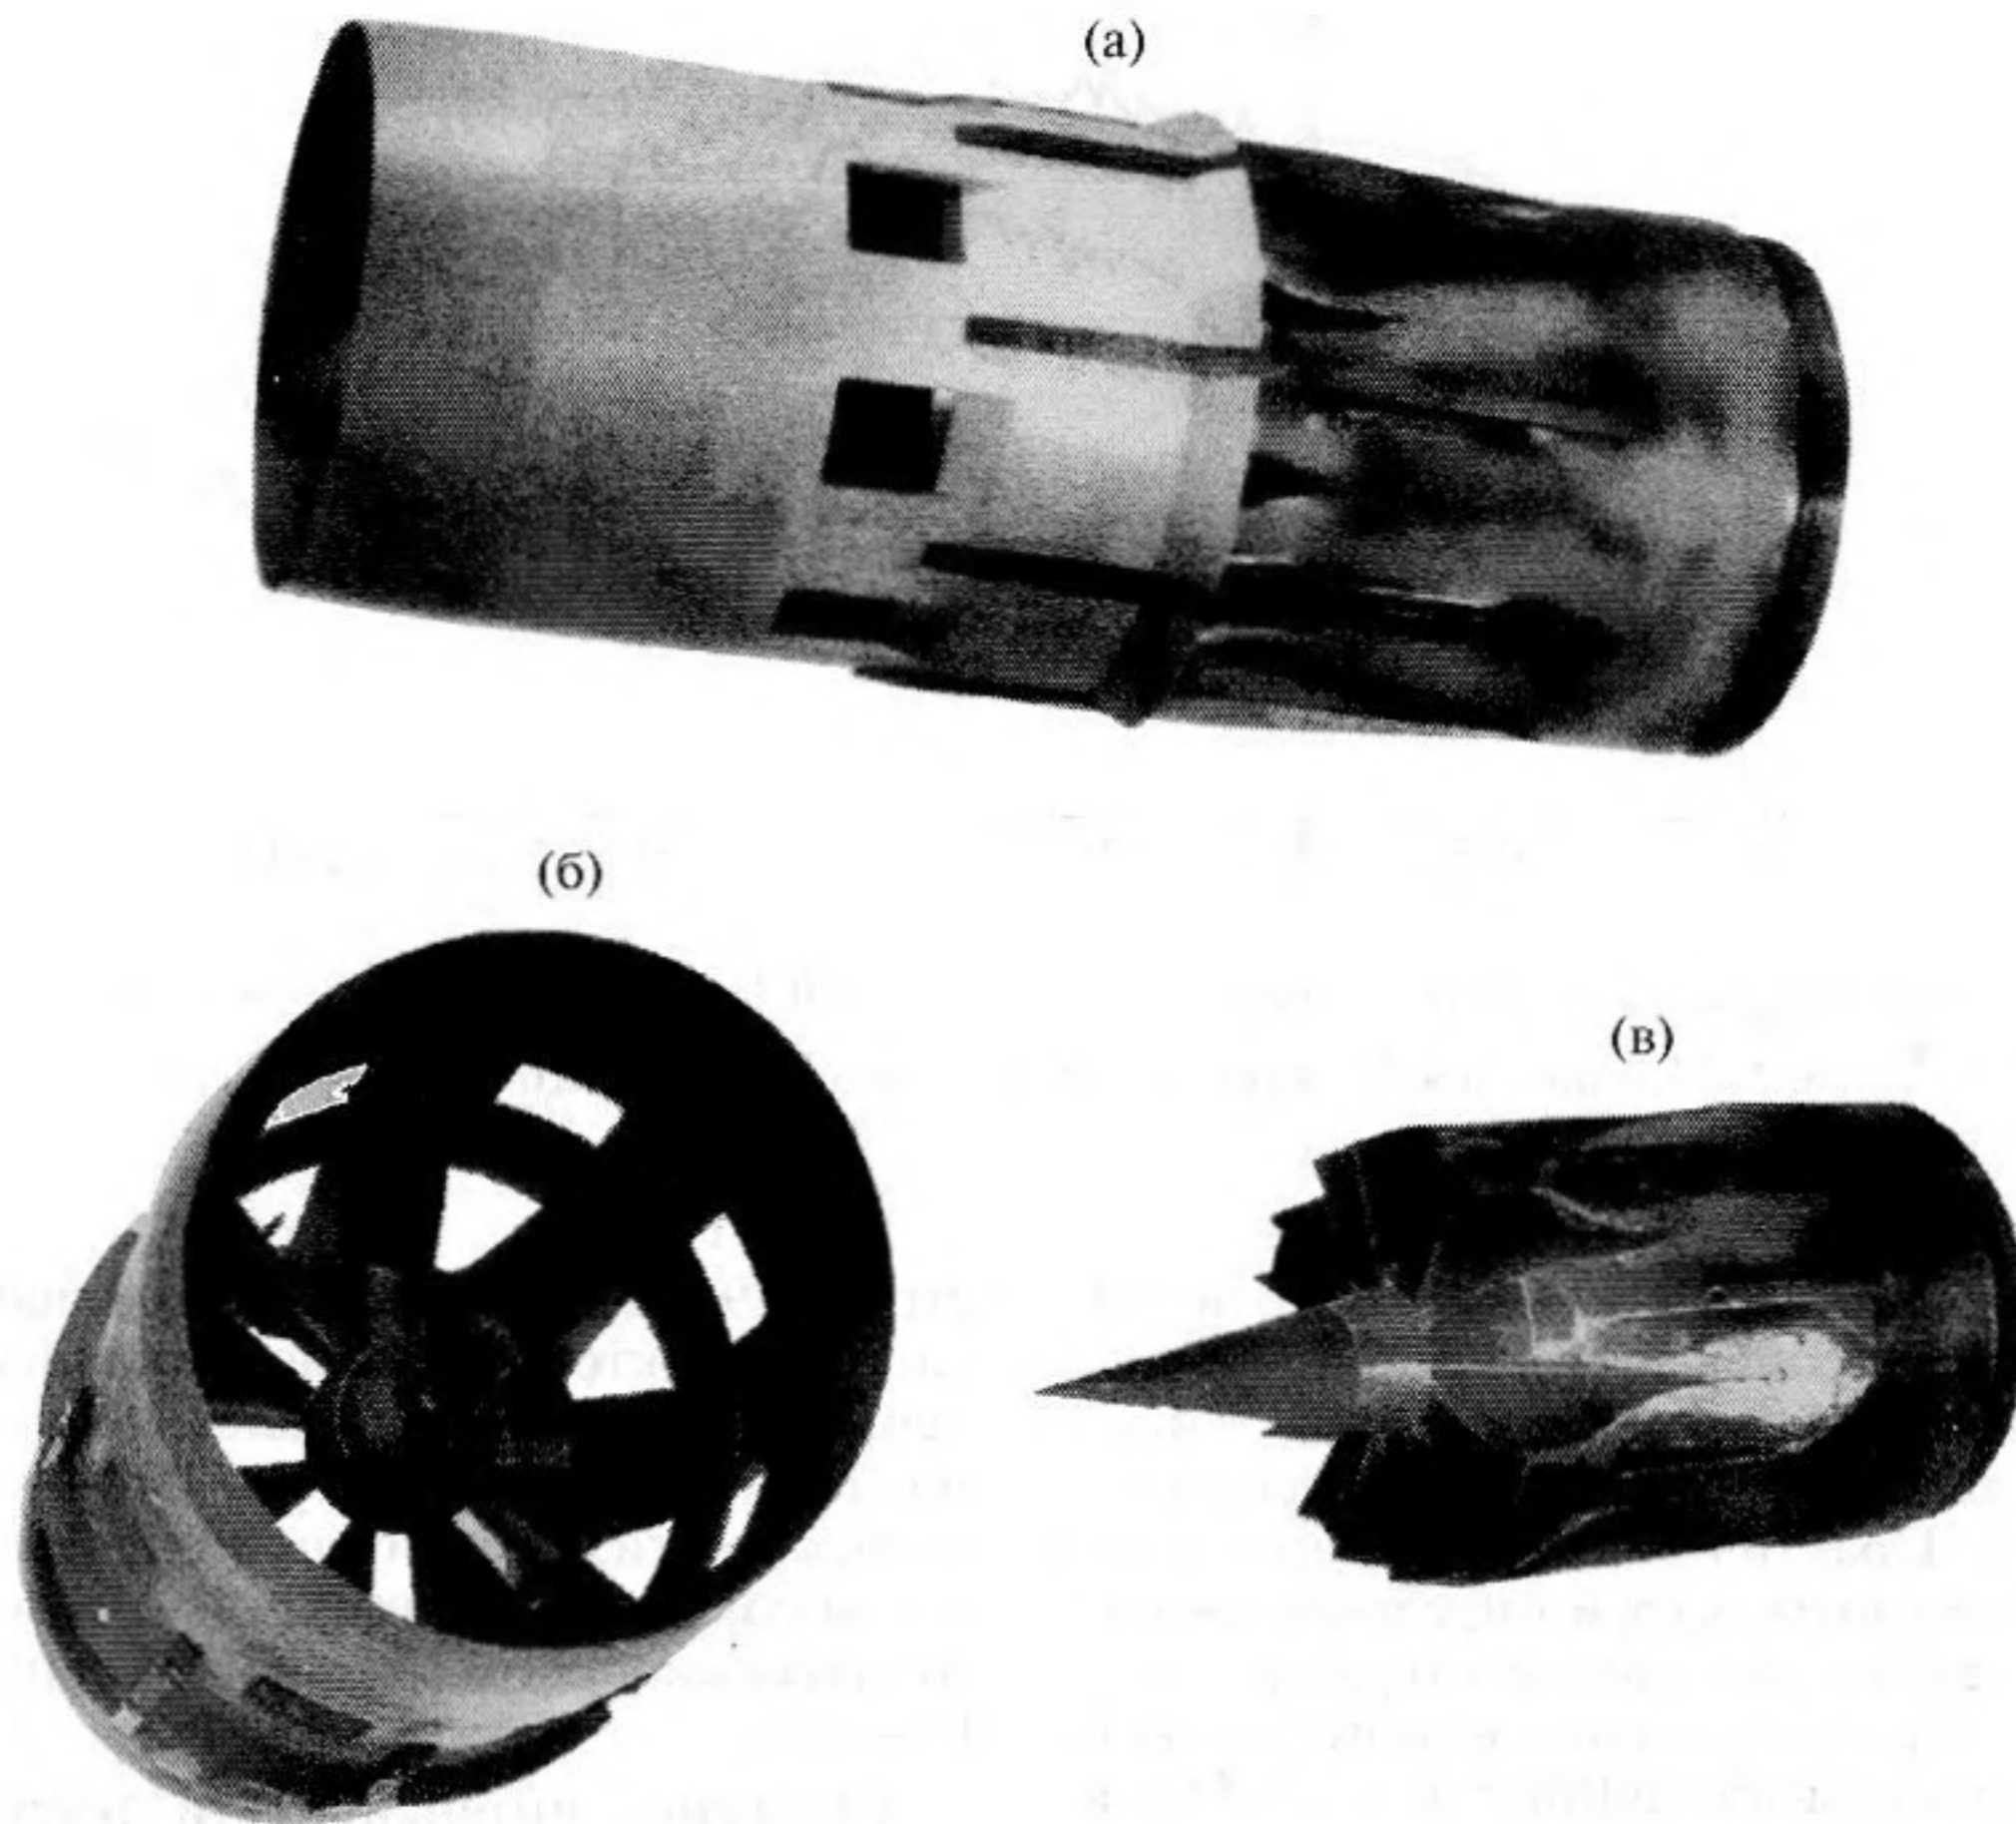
Общий вид (а) — эжекторного шумоглушащего сопла, (б) — эжектора с дополнительными окнами в боковой стенке, (в) — смесителя.
